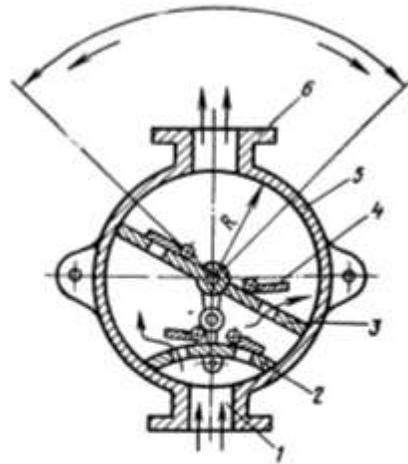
Схема ручного крыльчатого насоса Альвейлера: 1, 6 — всасывающая и нагнетательная трубы; 2 — неподвижная диафрагма; 3 — крыло; 4 — откидной клапан; 5 — корпус
